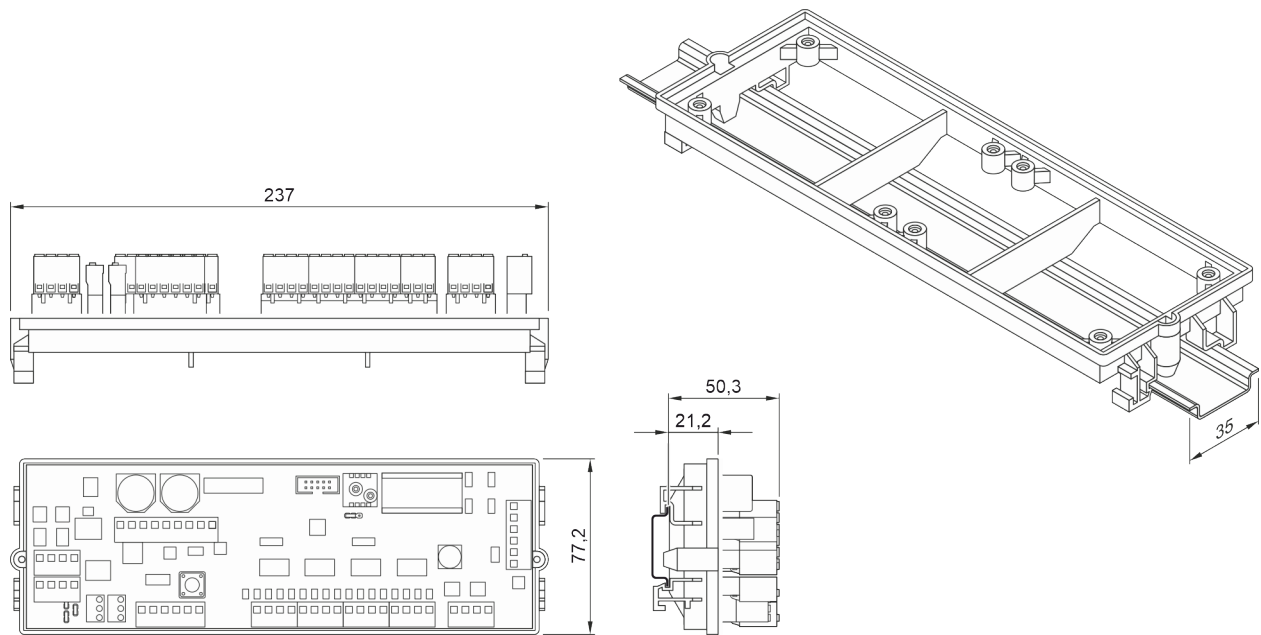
RM-V16.20-Platine auf Montageträger für Tragschienen-Montage
